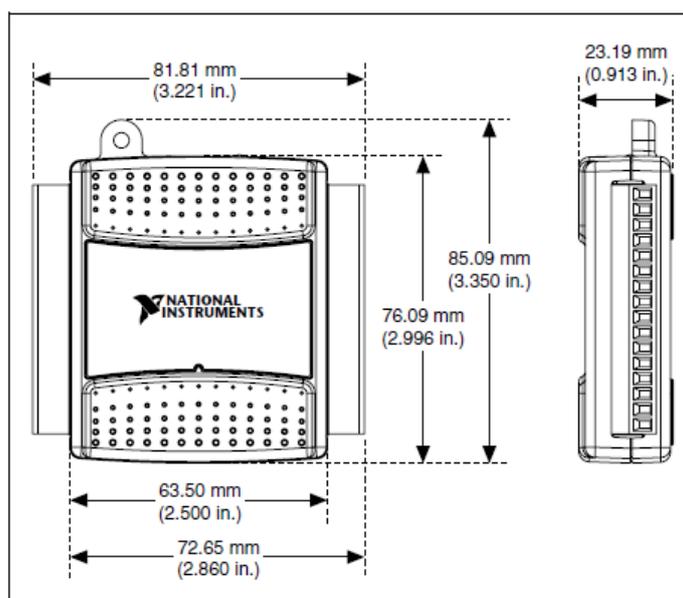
Dimensiones tarjeta NI-USB 6008 en milímetros (pulgadas)
